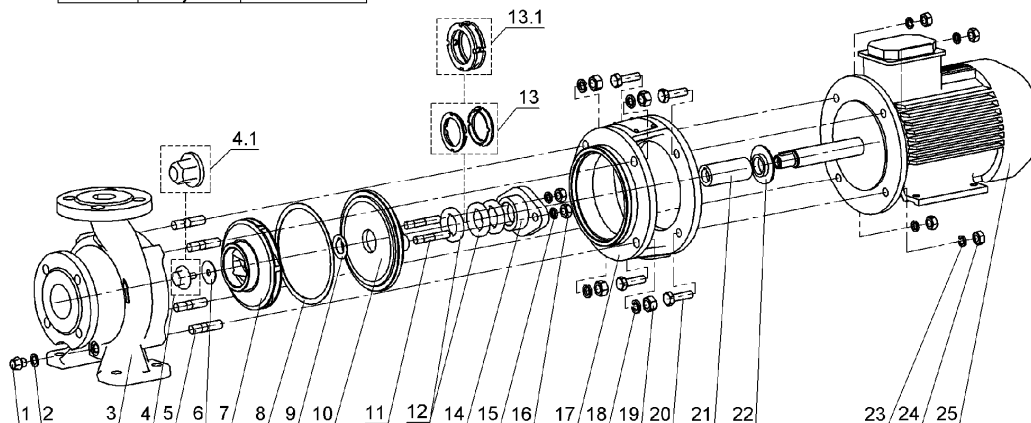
Устройство и схема разборки с сальниковой набивкой.
